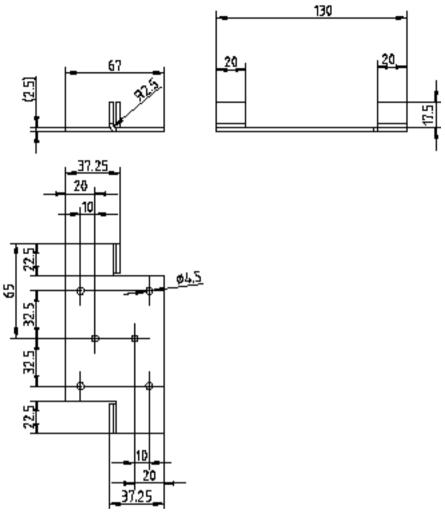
Soporte para montaje de pieza central de X-300EEC (medidas en mm) Material: chapa 2.0 DIN EN10152 DC01+ZE25/25
